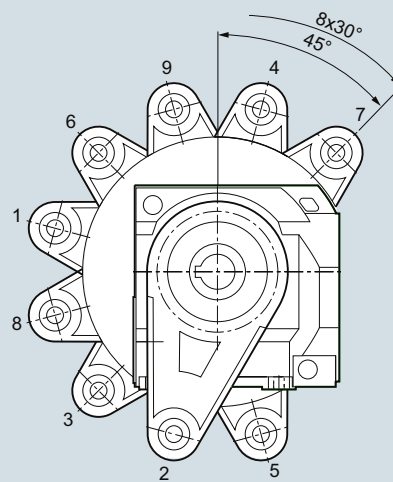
/9 Stirnradschneckengetriebe C in Aufsteckausführung
